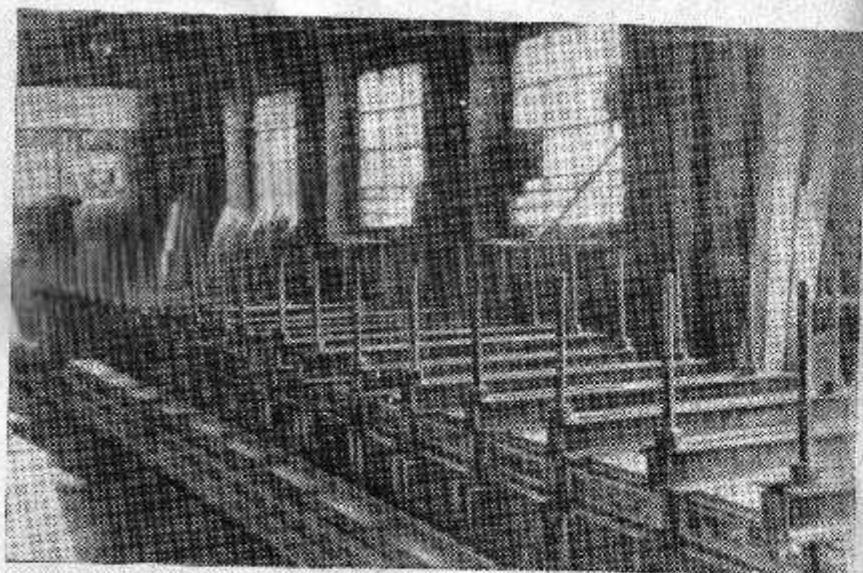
Стенд с винтовыми зажимами для запрессовки балок двутаврового профиля с перекрестной стенкой
